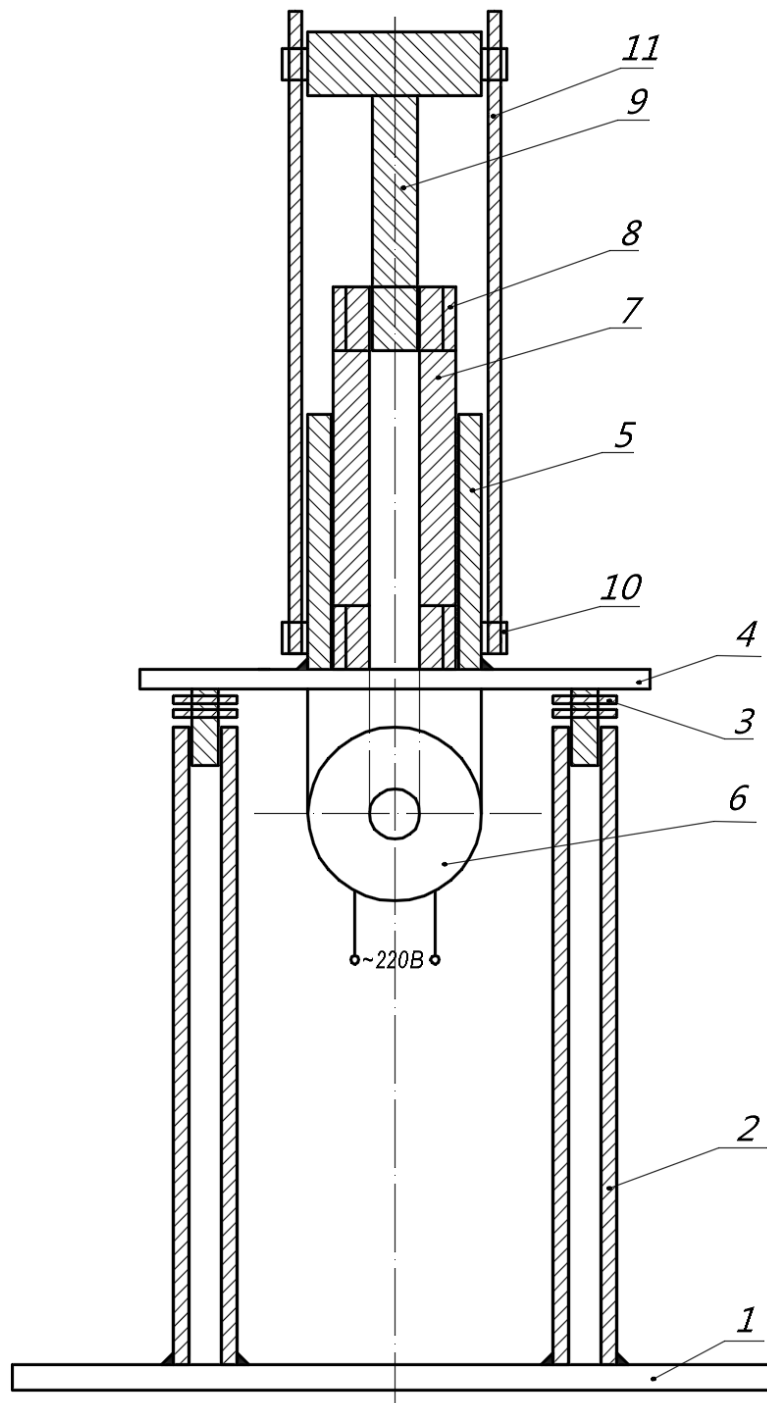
Схема лабораторного вибропресса [97].
